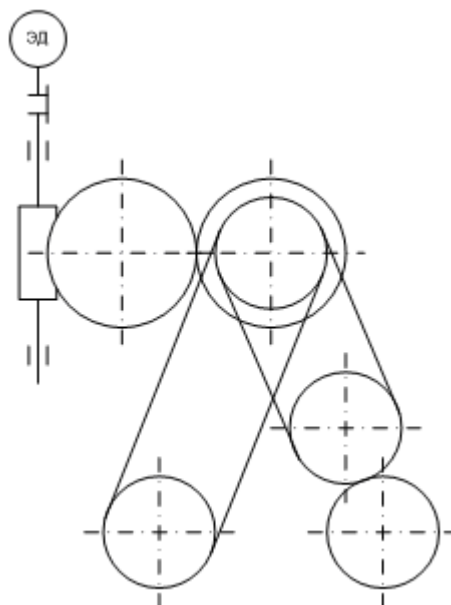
Кинематическая схема ориентаторов (боковых валиков)
